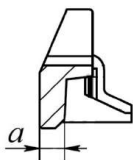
Поперечный разрез бокового изолятора сцеплений типа Pandrol Fastclip
